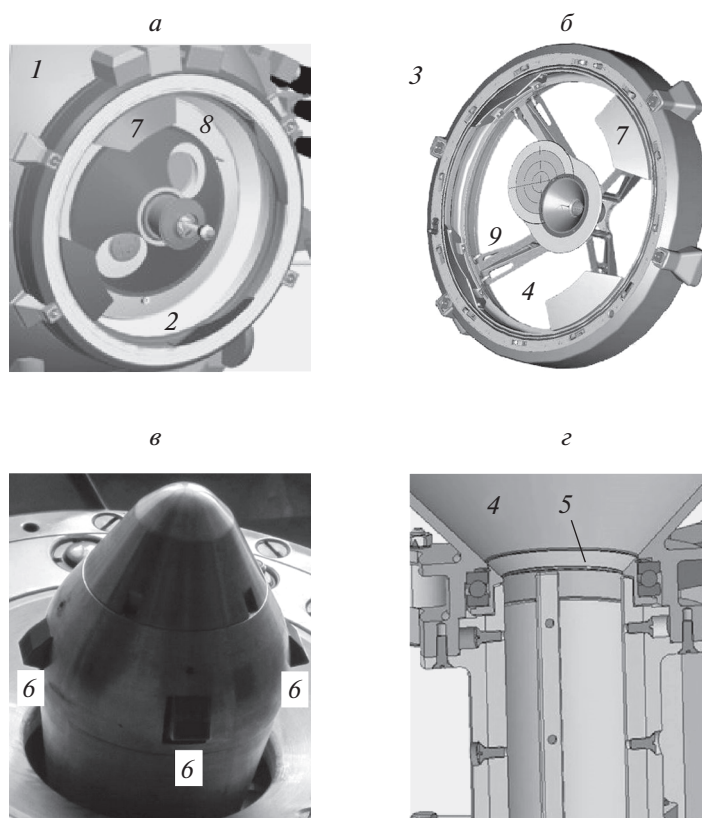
Активный и пассивный агрегаты для выполнения причаливания: *а* – активный СТА; *б* – пассивный СТА; *в* – головка захвата СтМ; *г* – гнездо приемного конуса
